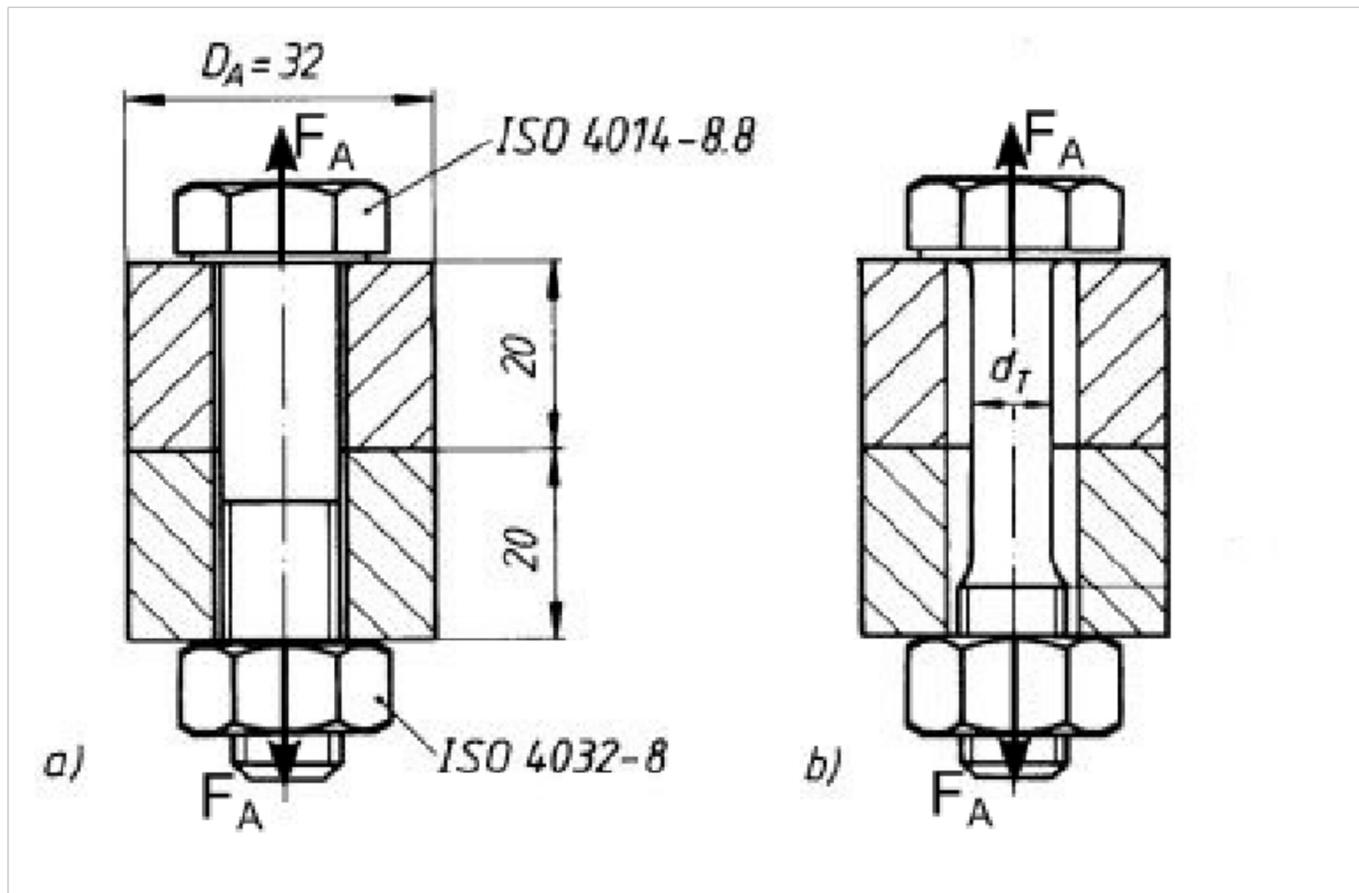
Durchsteckverbindung von zwei Platten mit Schaft- und Dehnschraube
